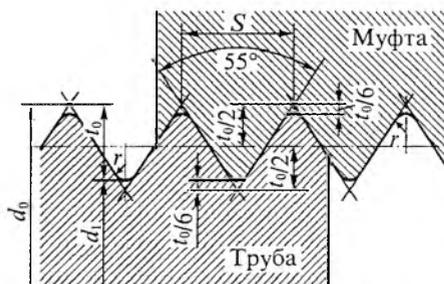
Трубная резьба (размеры указаны в миллиметрах): d_0 – наружный диаметр резьбы; d_1 – внутренний диаметр резьбы; t_0 – высота профиля; r – радиус впадины; S – шаг резьбы
